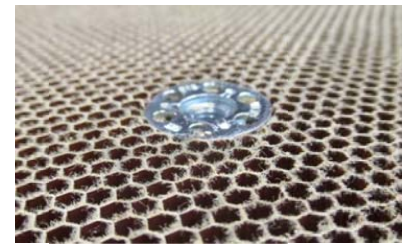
Ziel: Nach dem Eindrücken ist das Insert plan in den Wabenkörper integriert.
